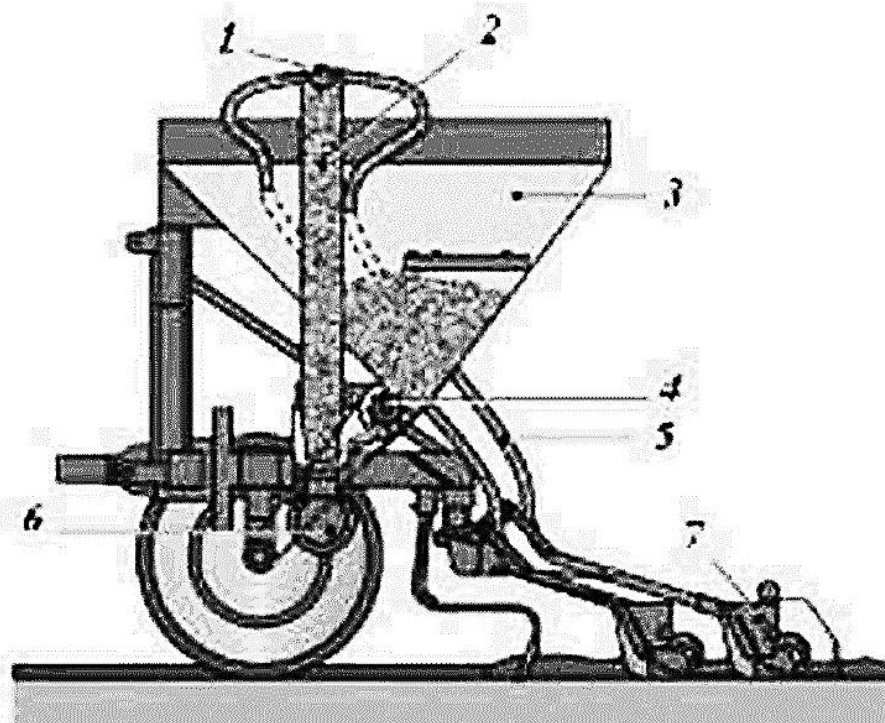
Схема работы сеялки СПУ: 1 – делительная головка; 2 – вертикальный трубопровод; 3 – бункер; 4 – дозатор семян; 5 – пневмосемяпровод; 6 – вентилятор; 7 – сошник
